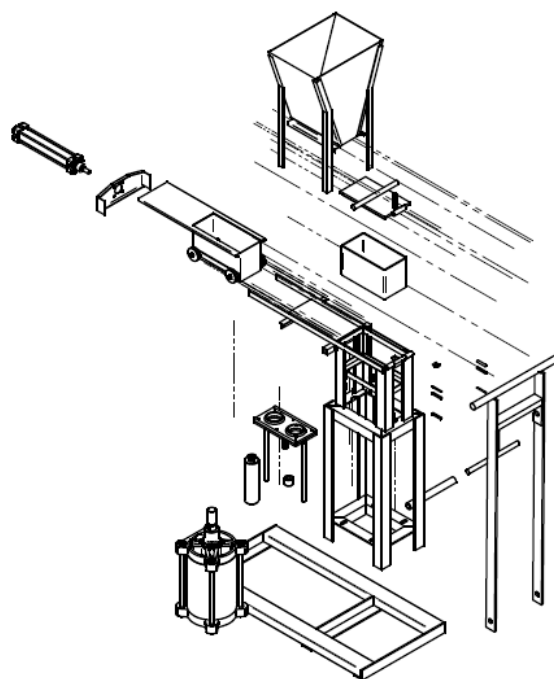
Vista explodida do desenho da máquina. Fonte: autores.
